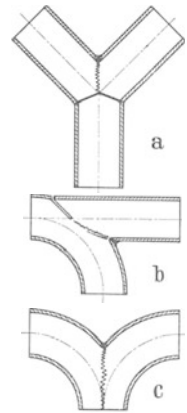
Schweißungen an Rohrabzweigungen.
